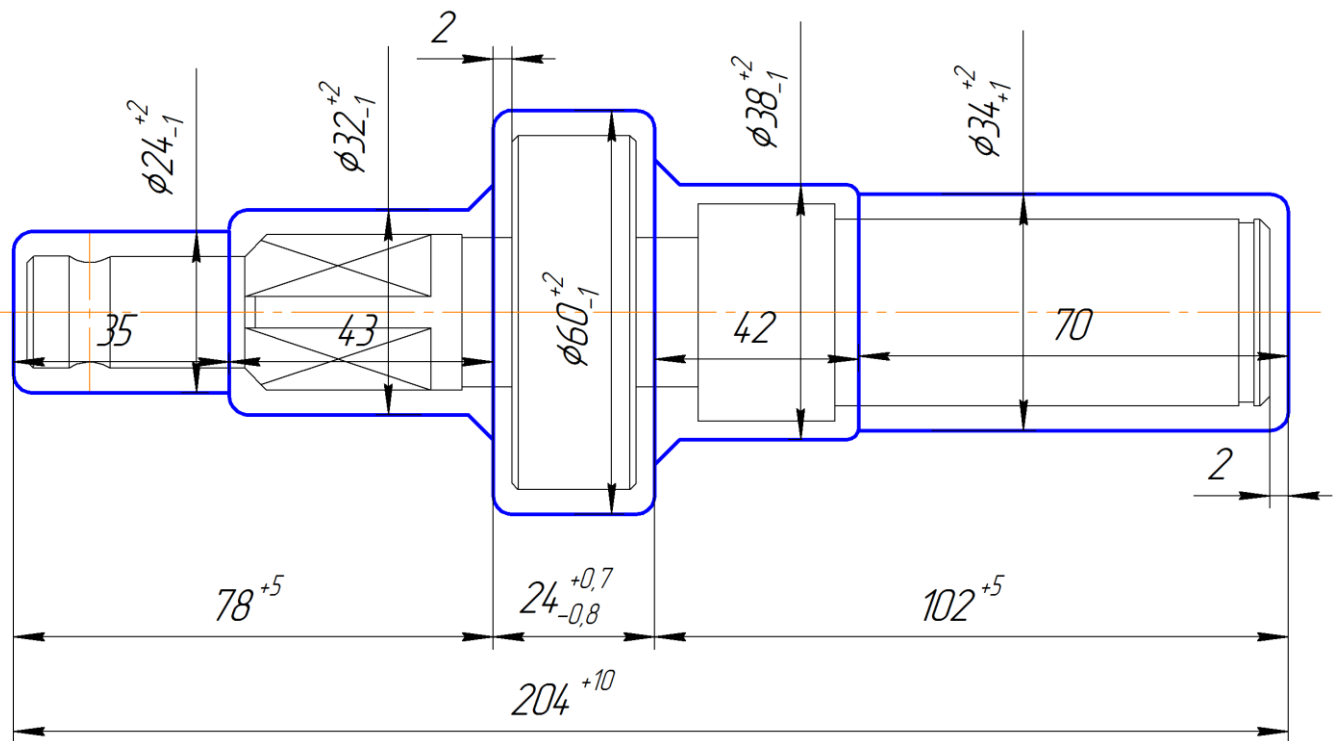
Ескіз поковки згідно ГОСТ 7505-75
